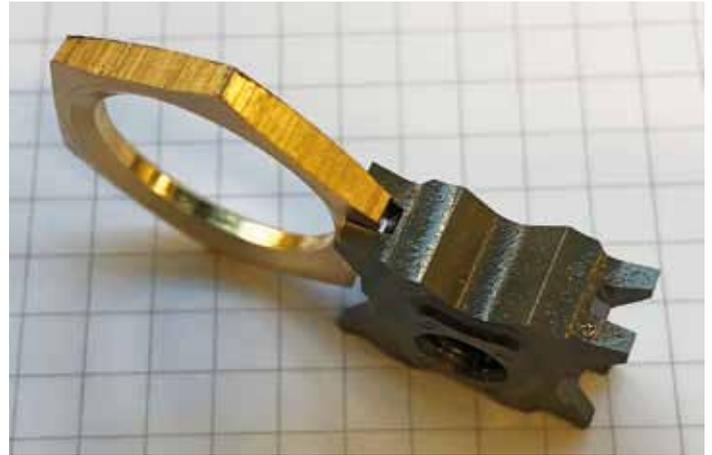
GoldFlex Fas-Stechwendeschneidplatte mit vier Schneidkanten zum Anfasen der Außenschrägen 2x10°
